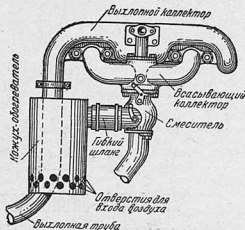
Схема устройства кожуха-обогревателя на автомобилях ГАЗ-42
